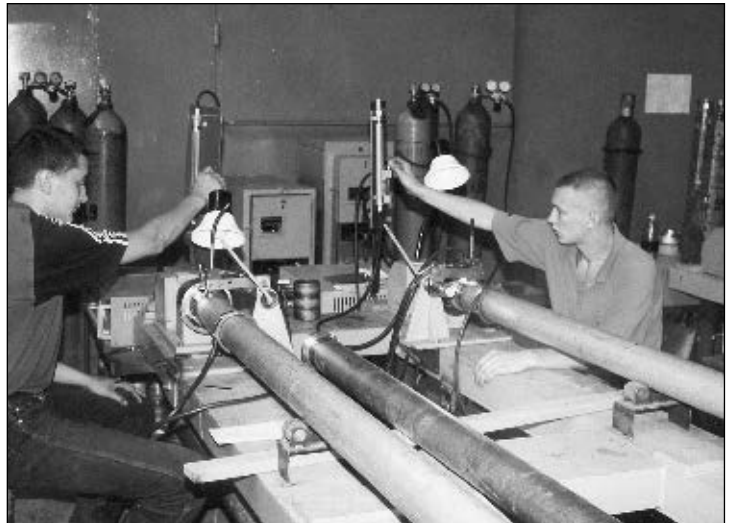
Рабочие места для автоматической сварки элементов труб
